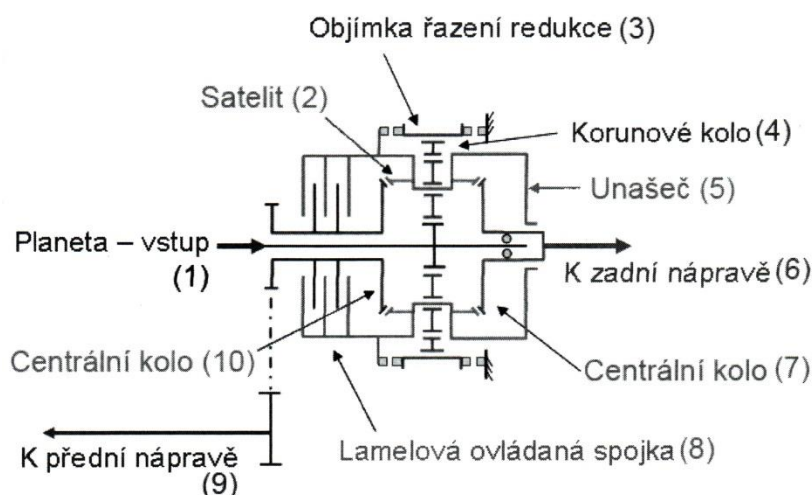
Schéma stálého pohonu všech kol s podélnou zástavbou a integrovanou rozvodovkou přední nápravy [4 str. 259]
